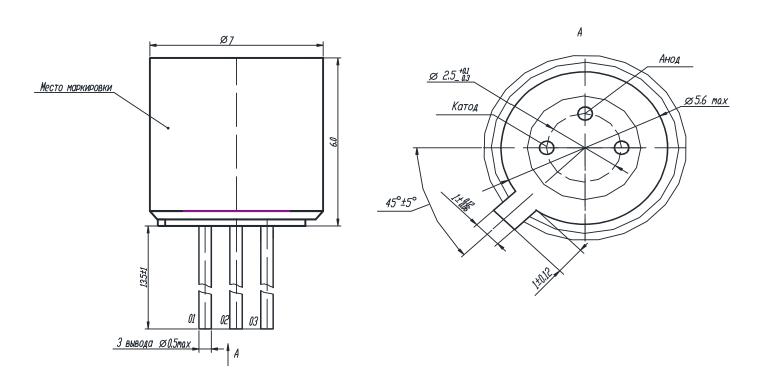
Габаритные размеры корпуса КТ-1-7
